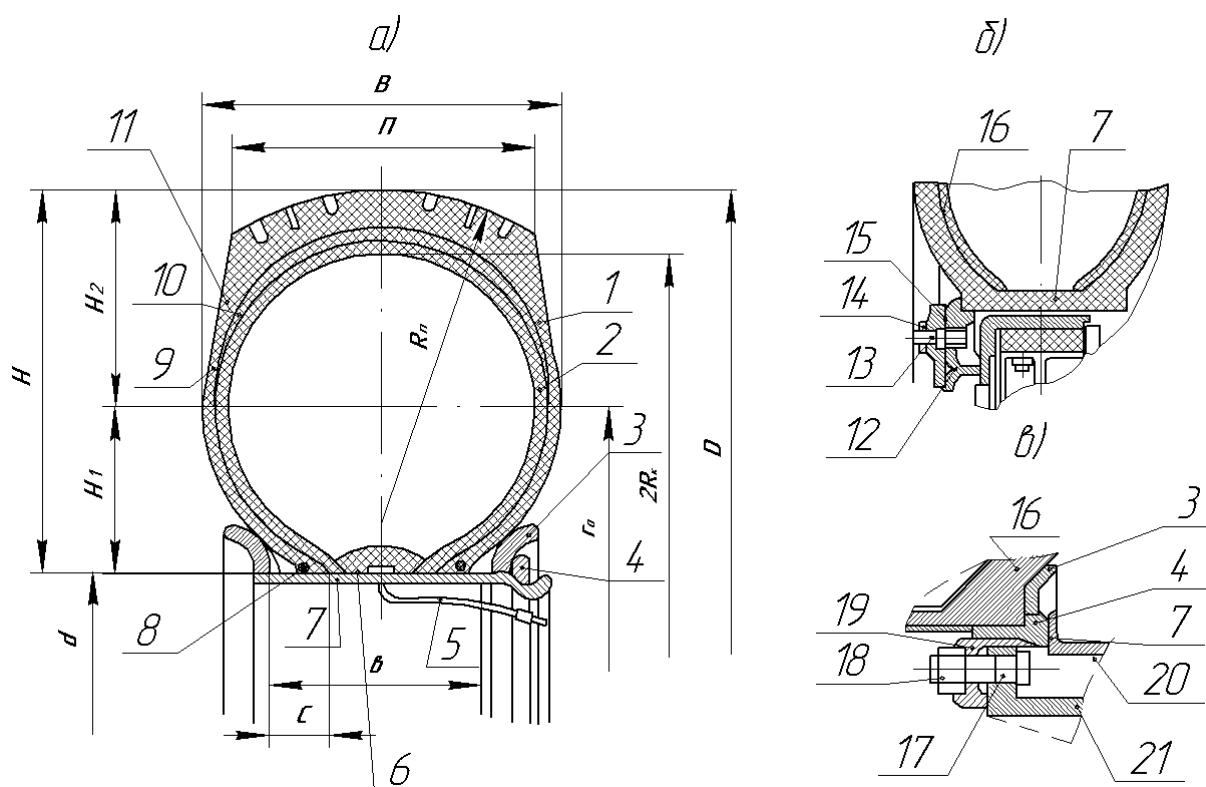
Конструктивні елементи бездискового пневматичного колеса тролейбусів ЗіУ–9: а – пневматична шина; б – кріплення одиночного (керованого) колеса; в – кріплення здвоєного (ведучого) колеса
